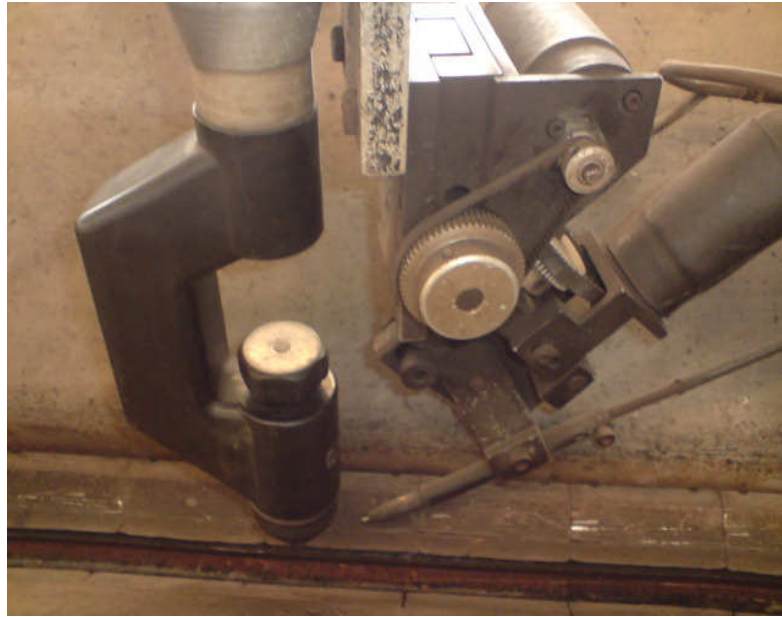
Tocha de soldagem Thermal Arc PWM 300 – Plasma Welding.
